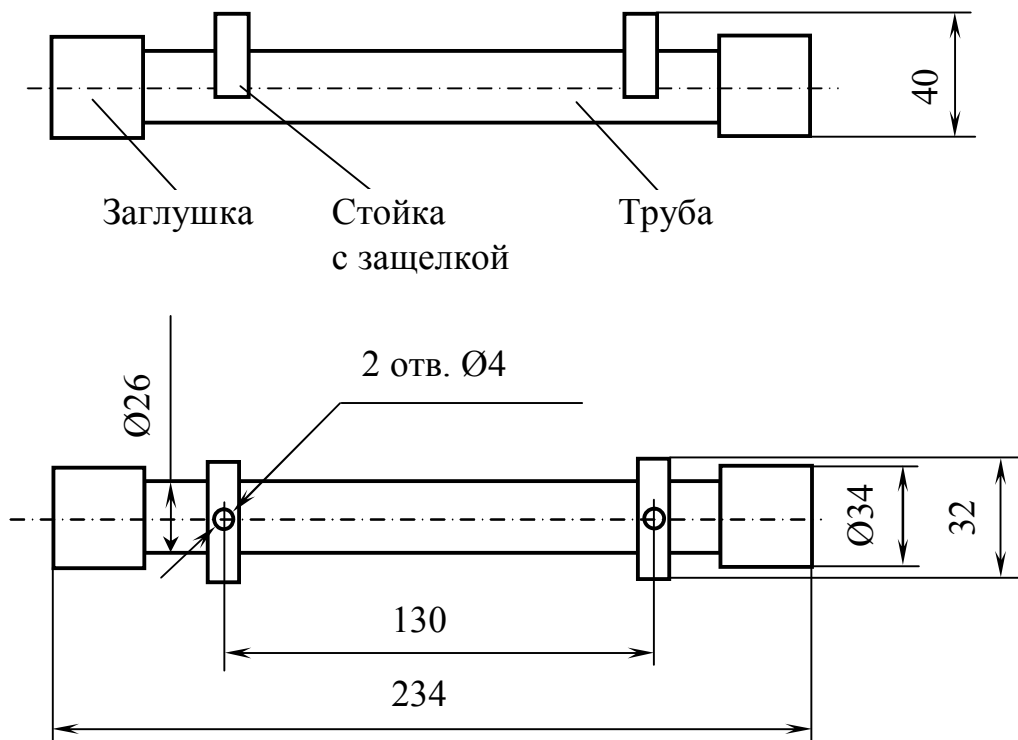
Габаритные и присоединительные размеры пенала модуля токового выхода
